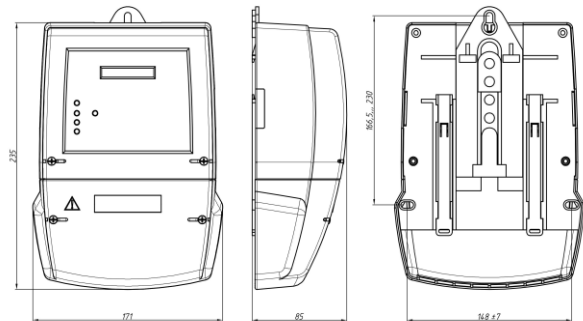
Загальний вигляд лічильника CE303-U в корпусі S35
